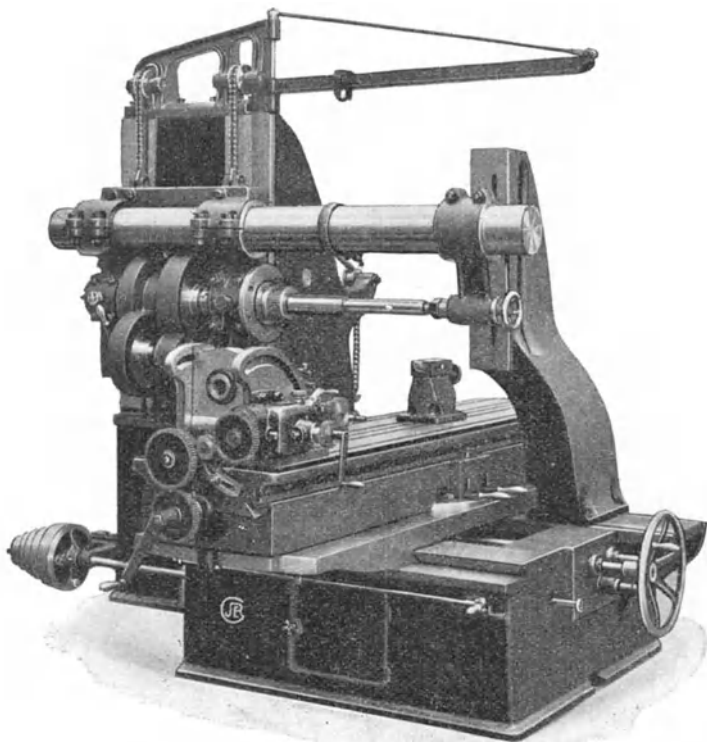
Die Universalfräsmaschine von J. E. Reinecker.
